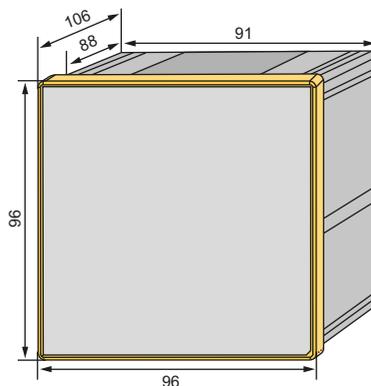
Maßbild PEM555 (Frontansicht)
